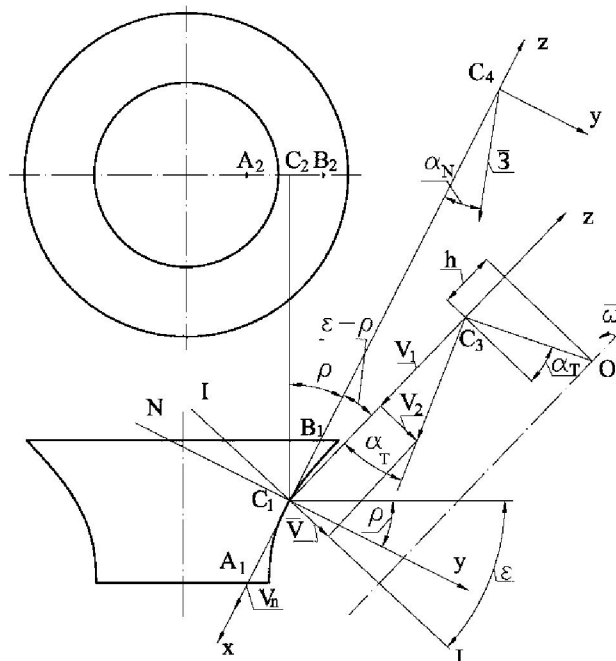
Обертання заготовки навколо своєї осі та рух різця в напрямку перпендикулярному осі деталі
